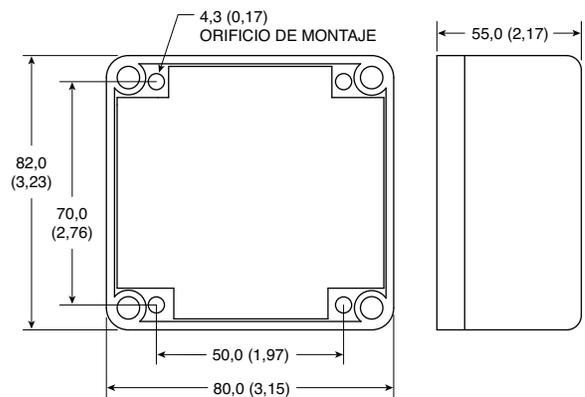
B. Dimensiones de montaje UWTC-2-NEMA, UWRTD-2-NEMA
